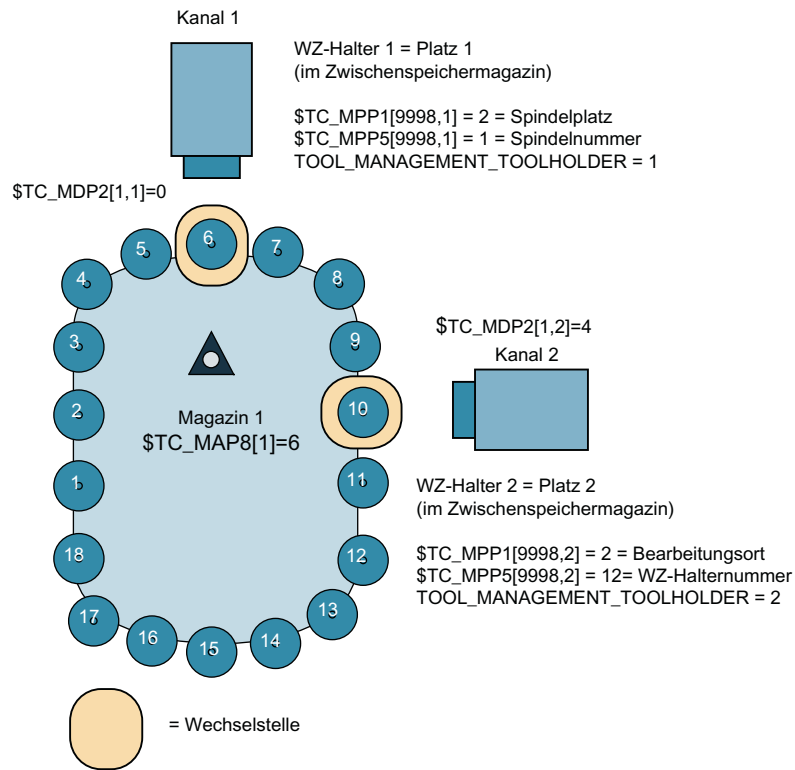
2 Kanäle mit je einem Werkzeughalter und einer TO-Einheit
